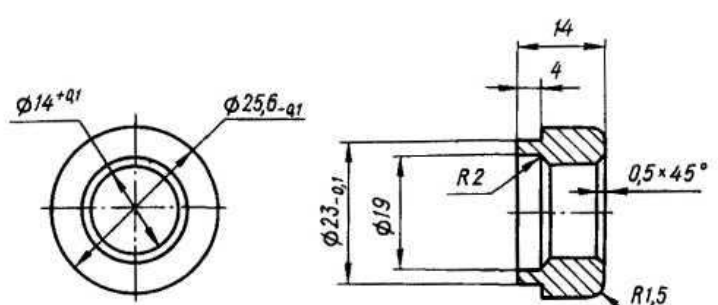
Оправка для выпрессовки и запрессовки втулки вала сошки рулевого механизма и втулок кронштейна маятникового рычага
